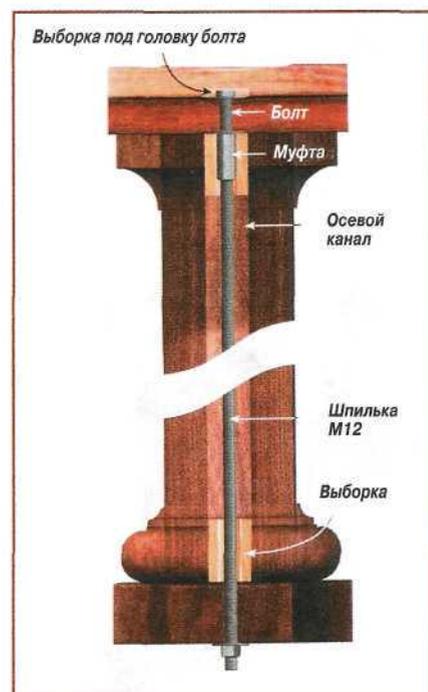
Сборка столика. Дополнительную опору столешницы, ножку и основание прочно свинчивают с помощью болта М12, муфты и резьбовой шпильки.
